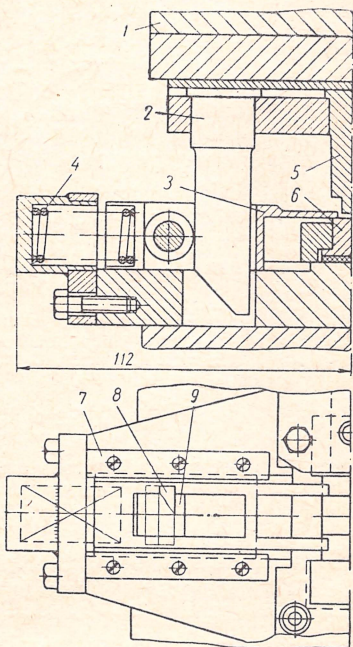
Безопасный сбрасыватель деталей с клиновым устройством
